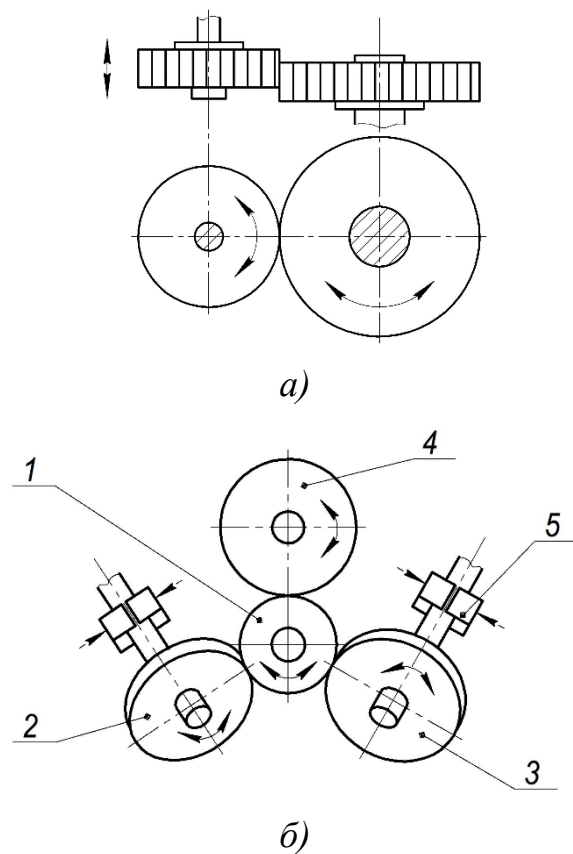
Схеми притирання зубів циліндричних зубчастих коліс:
